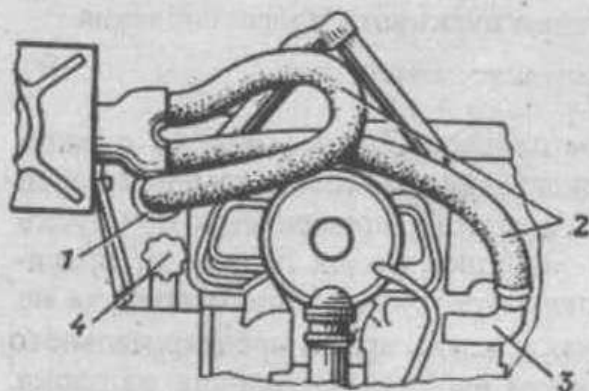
Подсоединение металлорукавов подогревателя (вид сверху):
